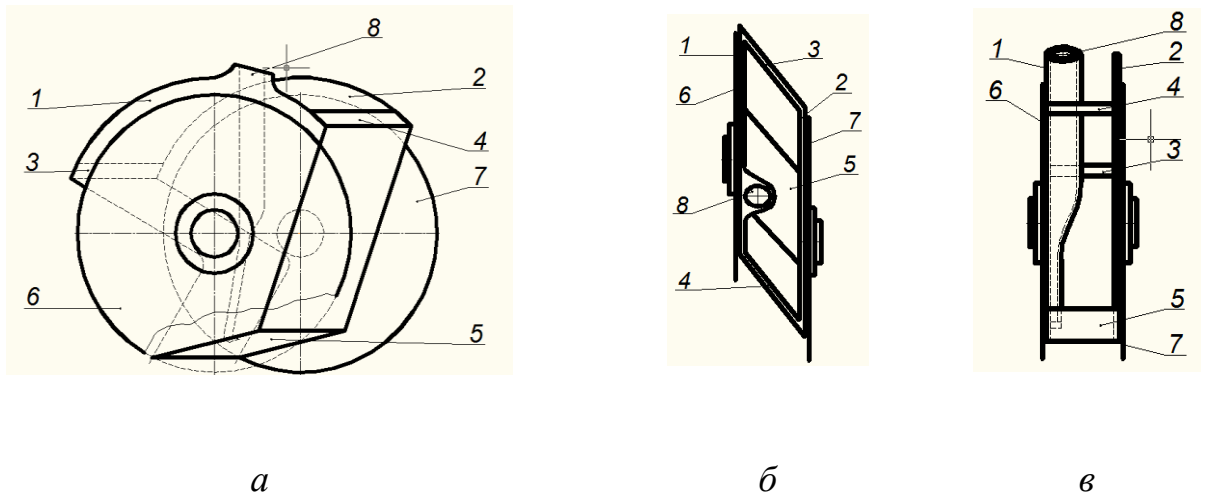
Сошник для разбросного посева: *а* – вид сбоку; *б* – вид сверху; *в* – вид сзади; 1, 2 – боковые стенки; 3, 4 – планки; 5 – лапа; 6, 7 – плоские диски; 8 – патрубок
